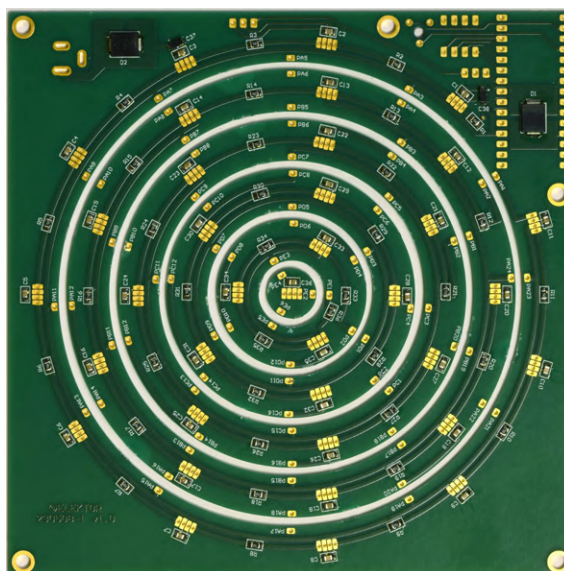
Tous les CMS sont soudés sur les faces arrière des PCB : R1...R36, C1...C38, D1 et D2.
